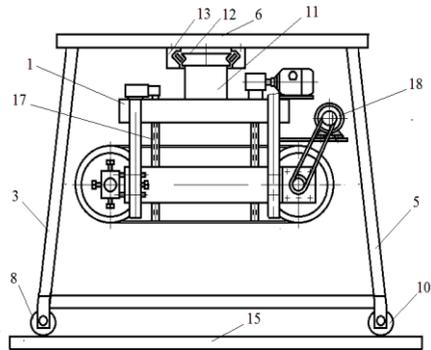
Общий вид ленточнопильного станка (вид сбоку при повороте пильного блока на 90 градусов)
